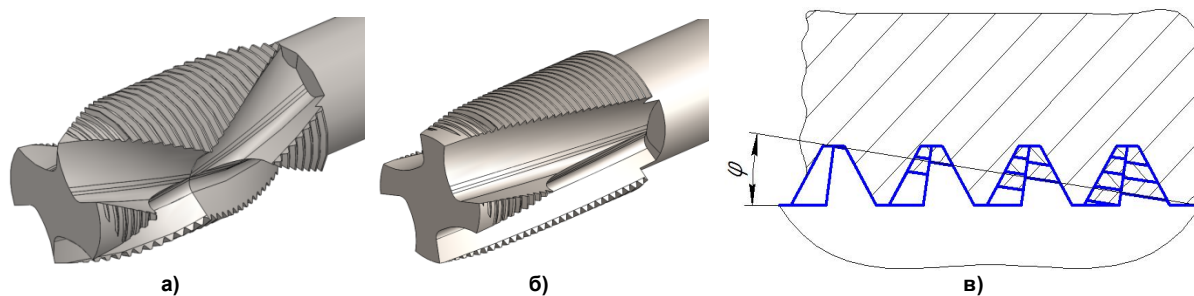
Метчики для нарезания резьб в композитных заготовках и схема срезания припуска [18]
